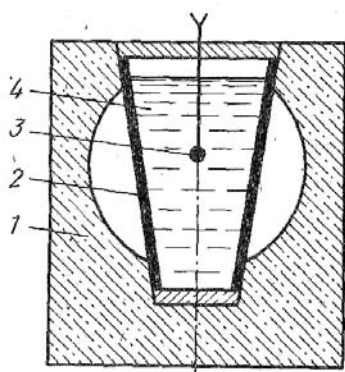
Схема бассейна для одноразовой штамповки взрывом:
